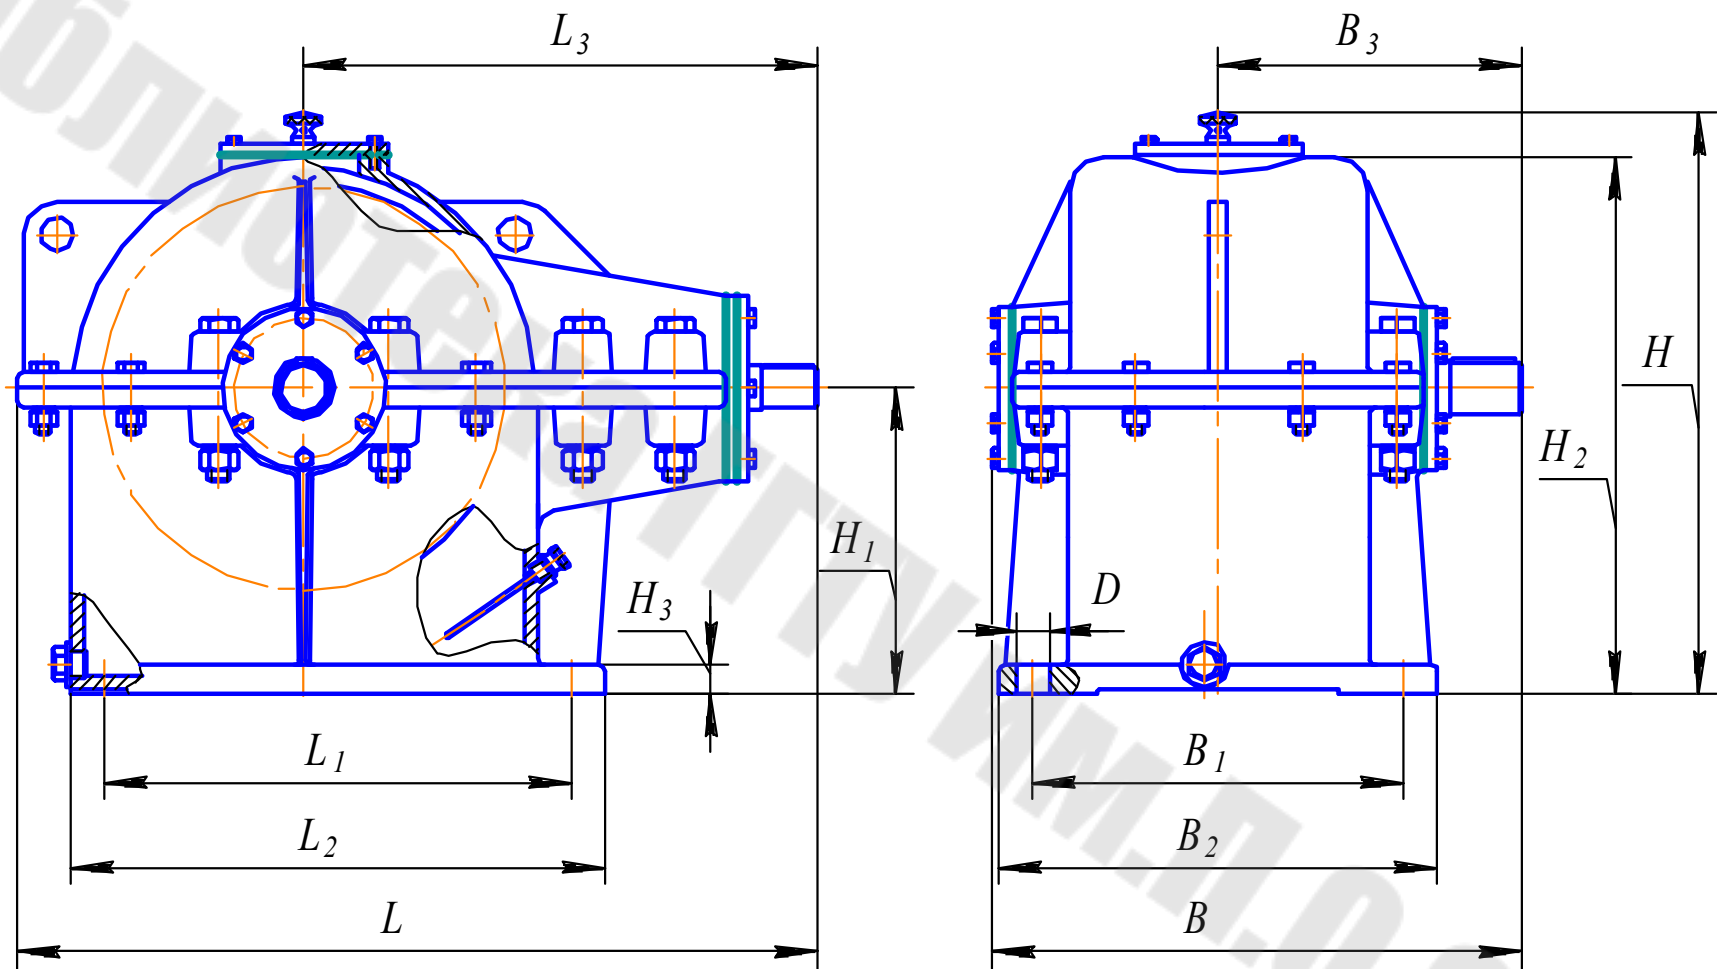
Габаритные и присоединительные размеры одноступенчатого конического редуктора
